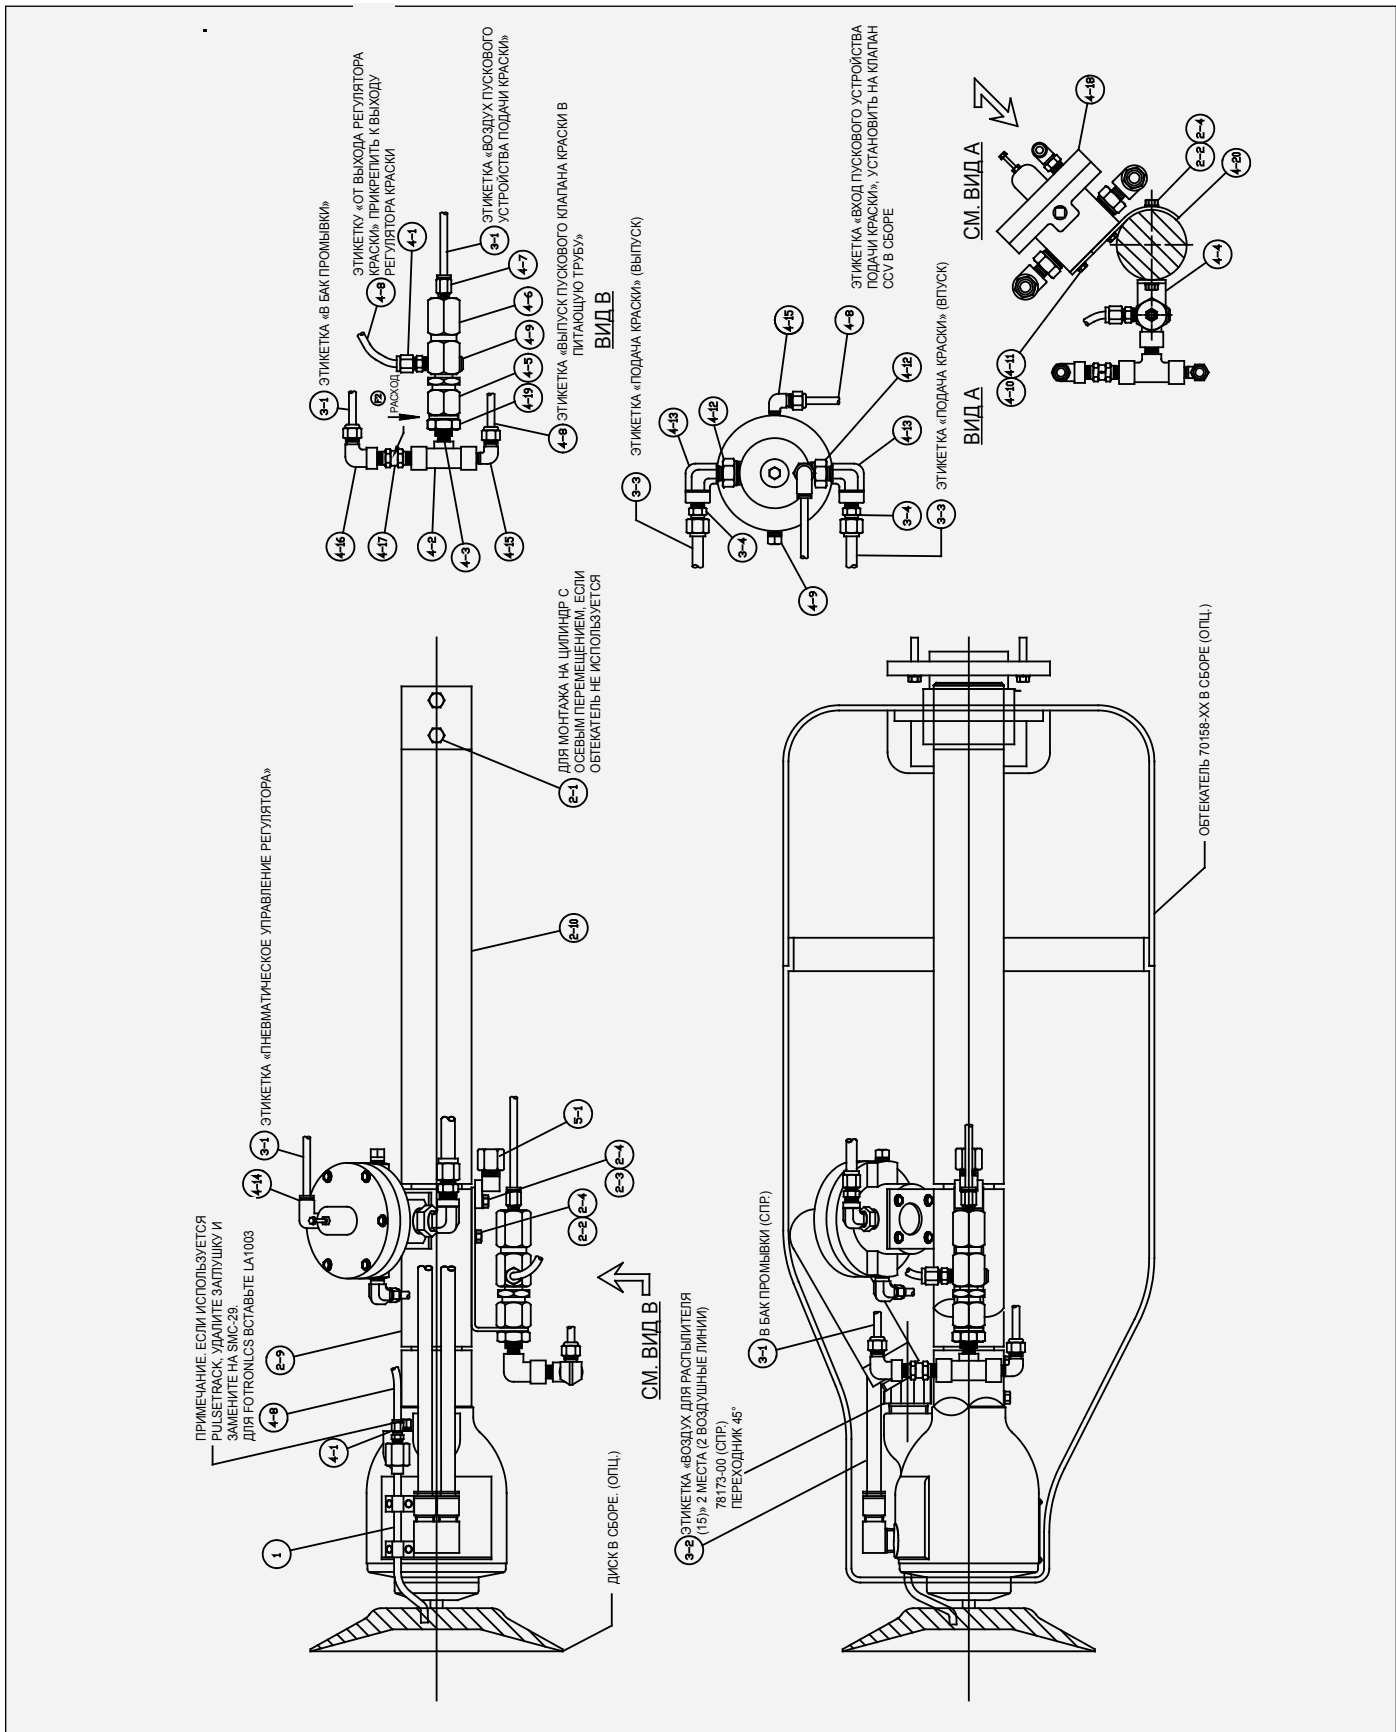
Аппликатор 70990-07 Turbodisk в сборе, только пусковой клапан
